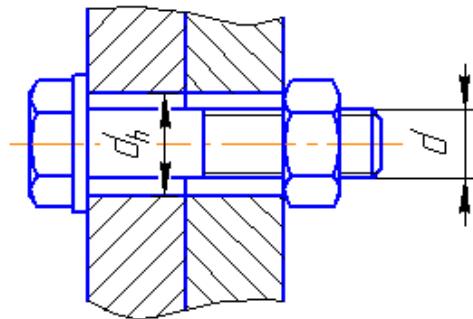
Конструктивный зазор между стержнем болта и отверстием в деталях
